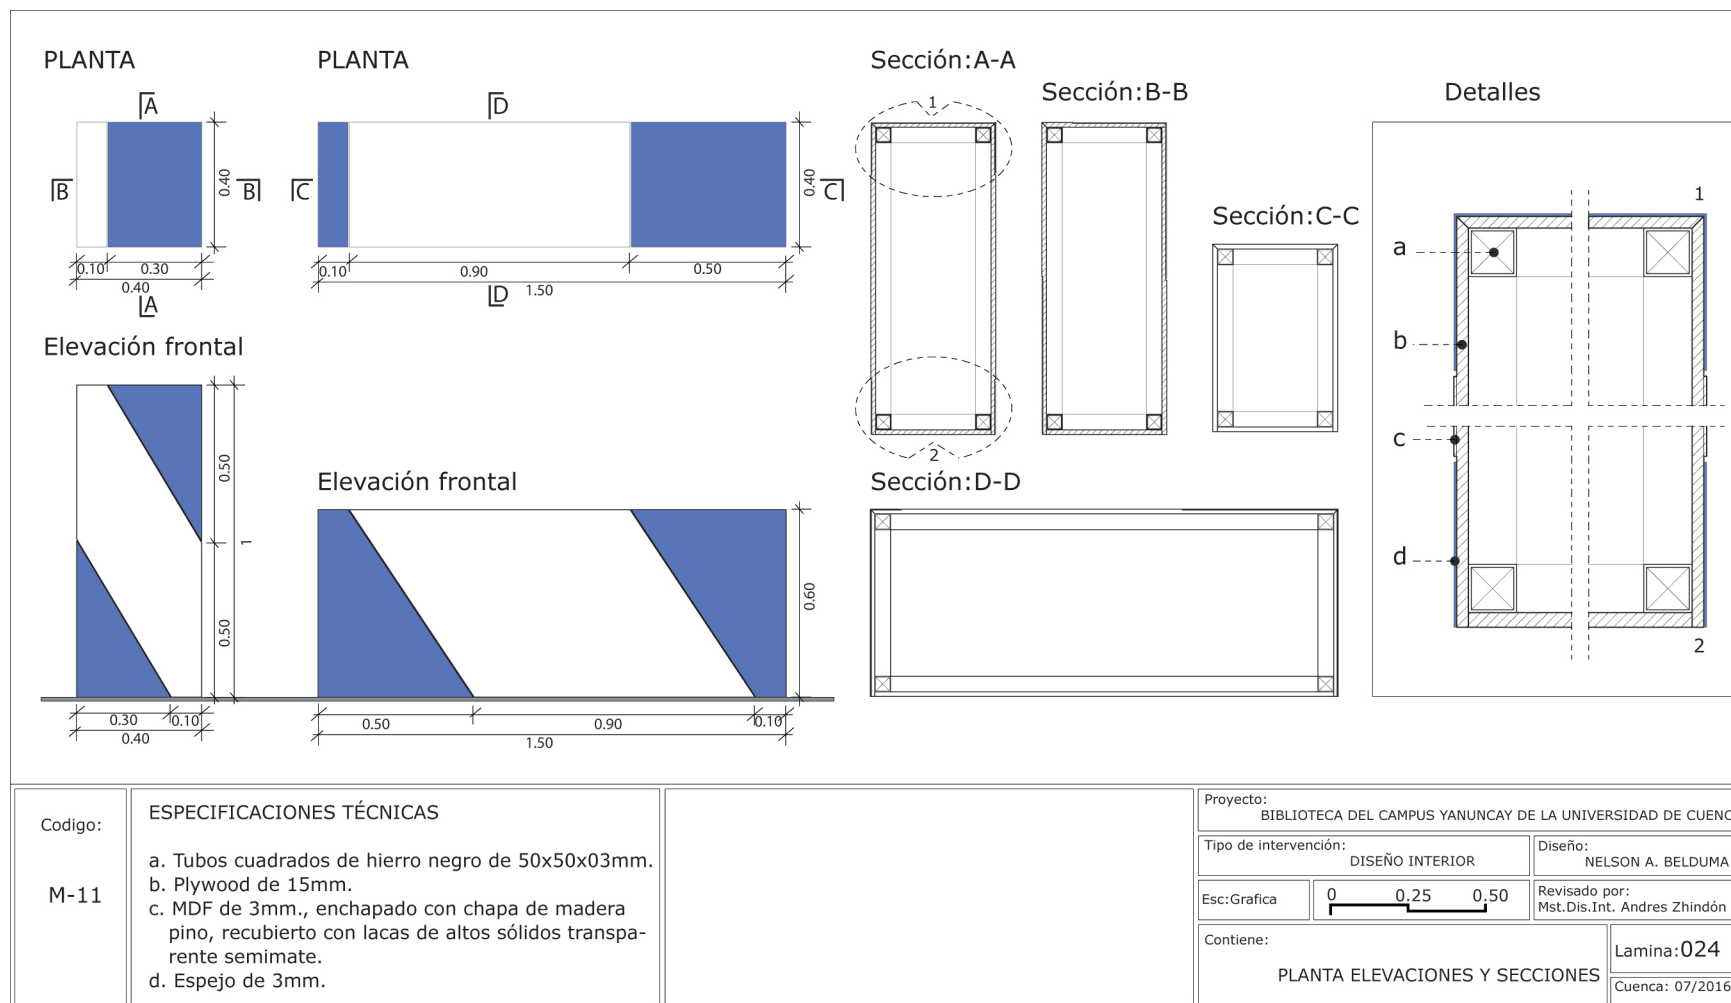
Planta, elevaciones y secciones. Área de exposición. M-11.
